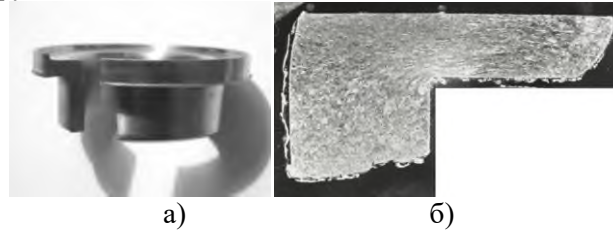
Вид заготовки: а) заготовки, отриманої обкочуванням за схемою рис. 2, б; б) мікроструктура фланця до моменту утворення тонкостінного елемента
